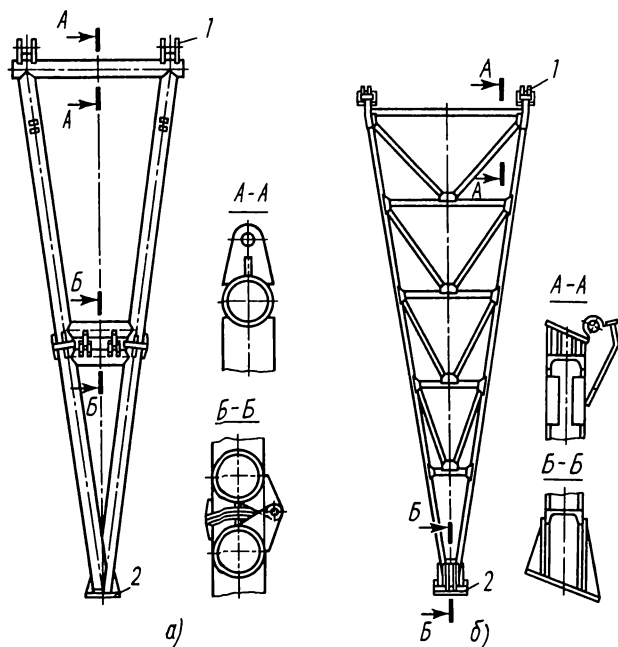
Опоры козлового крана из труб (а) и двутавровых балок (б)
